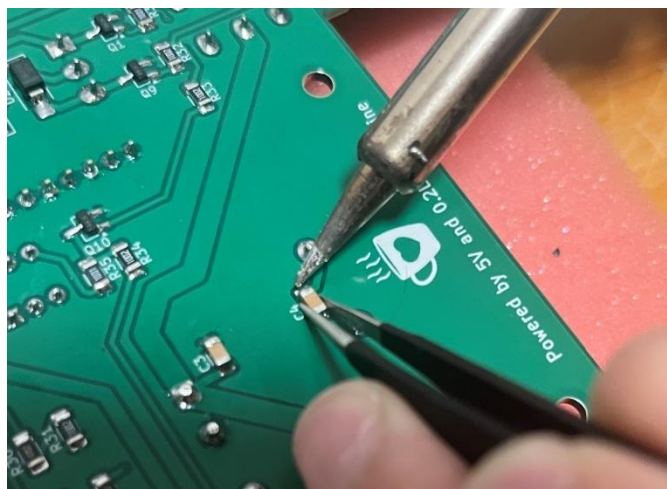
Processo soldadura dos componentes no PCB
